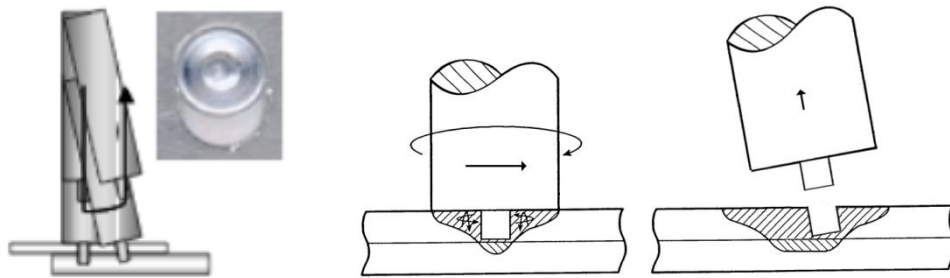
Ferramenta para soldagem Plunge FSSW indicando direção de rotação, movimentação vertical, lateral e área soldada resultante (OKAMOTO 2005).
